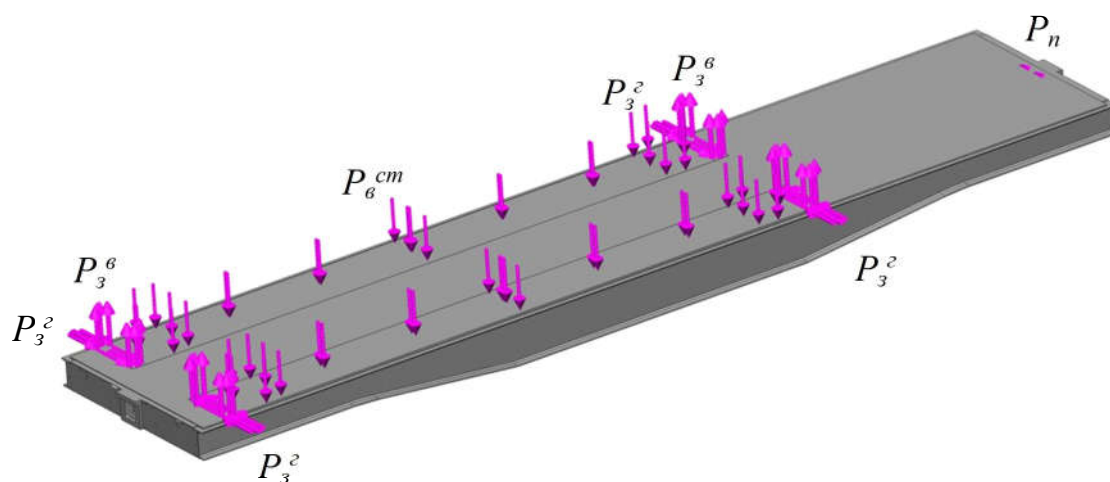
Розрахункова схема несучої конструкції вагона-платформи
